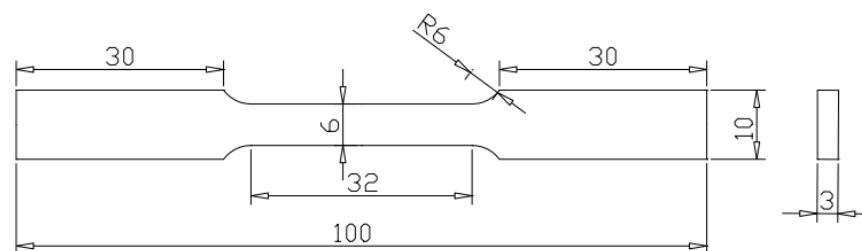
Dimensões do corpo de prova (mm) utilizado para o ensaio de tração.
